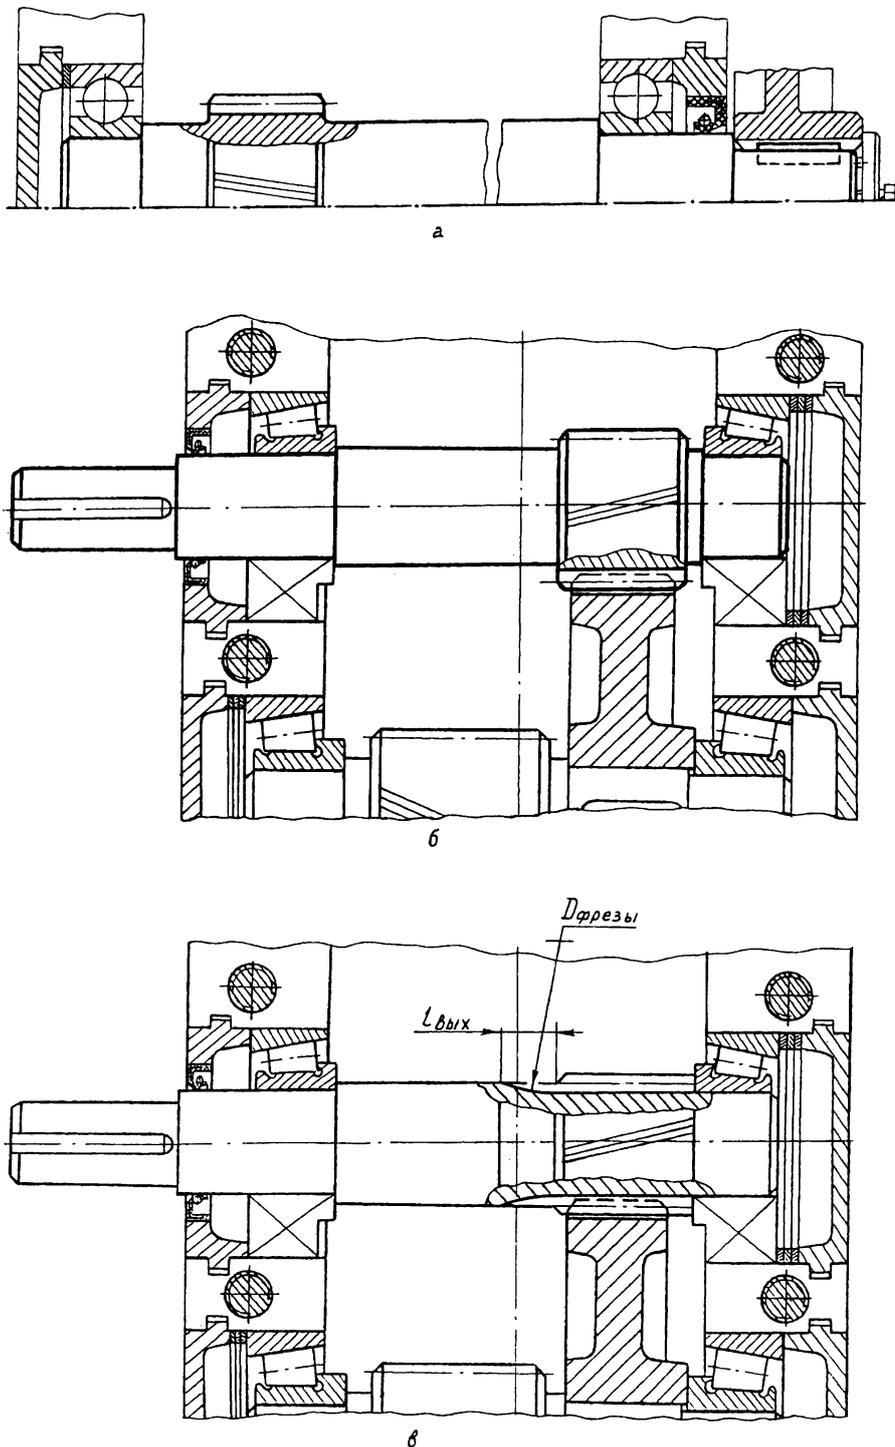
Примеры конструкций подшипниковых узлов валов, зафиксированных по схеме «враспор» (крышки подшипников – закладные)
